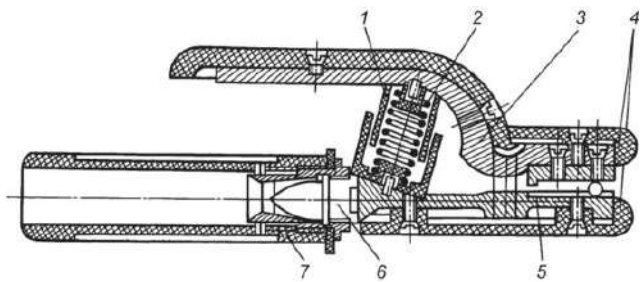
Электрододержатель ЭП: 1 – защитный пружинный колпачок; 2 – пружина; 3 – рычаг с верхней губкой; 4 – теплоизоляция; 5 – нижняя токоведущая губка; 6 – конус резьбовой втулки крепления сварочного кабеля.
